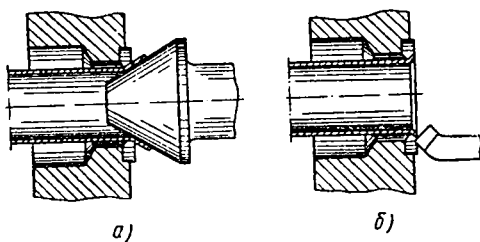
Отбортовка концов труб по фаске приваренного фланца или упорного кольца (а) и проточка привальной поверхности и прорезка уплотнительных канавок на фланцах и упорных кольцах (б)
